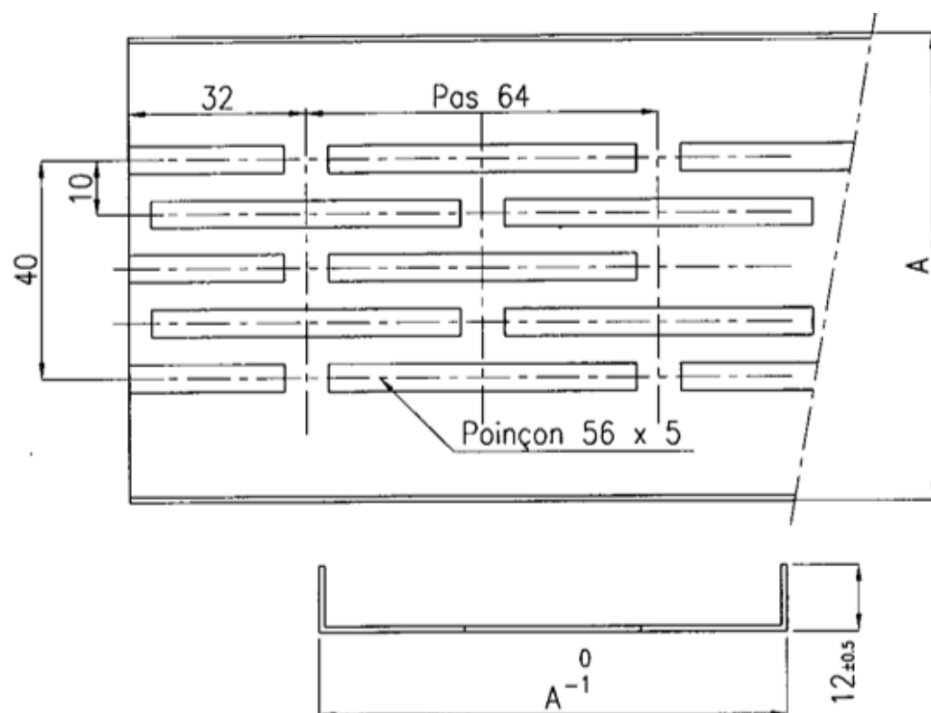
Schéma 1 – Panneaux parements – Profilage MF
